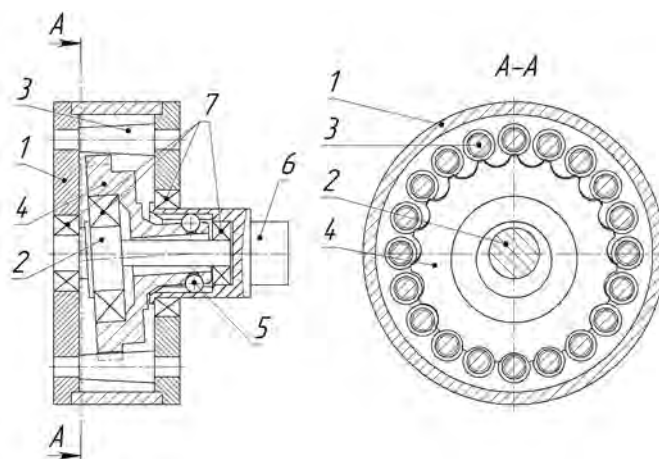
Конструктивная схема планетарной прецессионной передачи: 1 – корпус; 2 – вал эксцентриковый; 3 – конические ролики корпуса; 4 – спутник; 5 – угловая муфта; 6 – вал выходной; 7 – опорные подшипники
